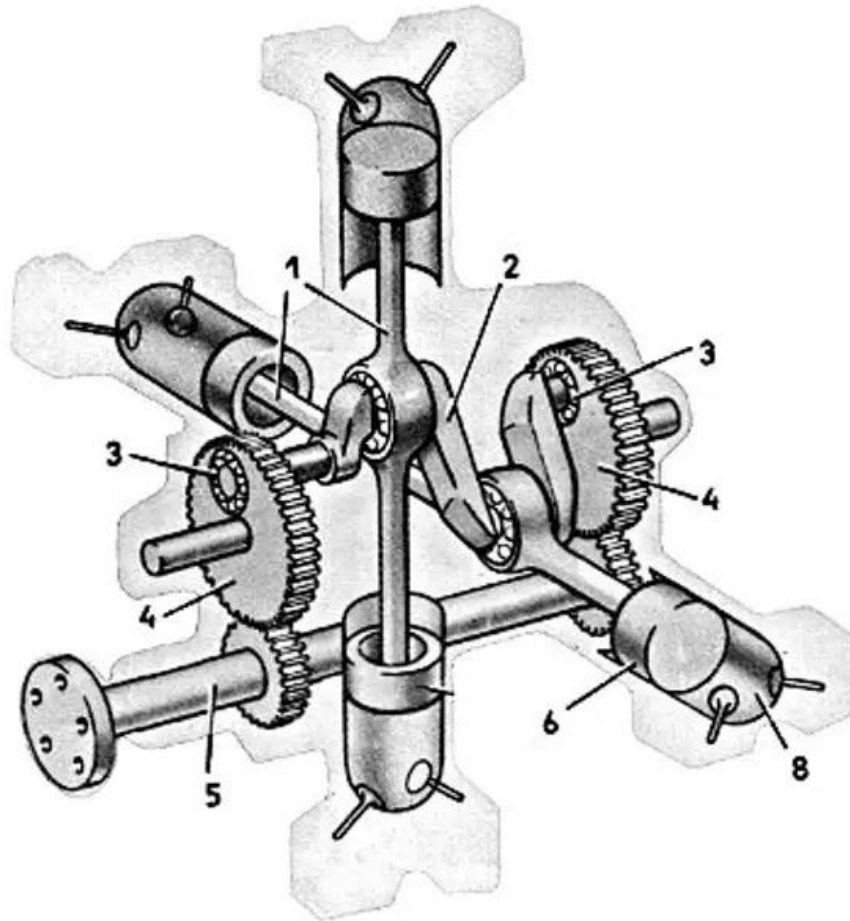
Принципиальное устройство бесшатунного двигателя: 1 – поршневой шток; 2 – коленчатый вал; 3 – подшипник кривошипа; 4 – кривошип; 5 – вал отбора мощности; 6 – поршень; 7 – ползун штока; 8 – цилиндр
